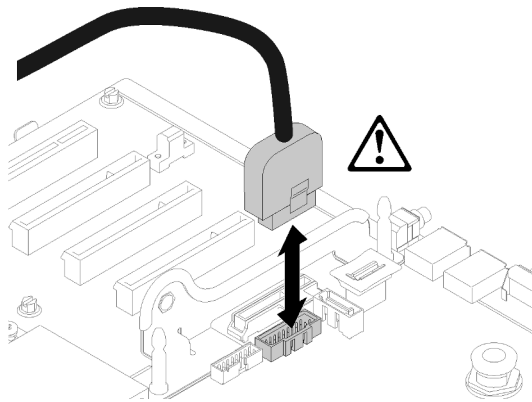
Cable USB 2.0 y cable del panel frontal del operador
